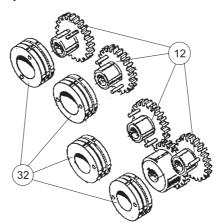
/7b Ersatzrollen Aluminium / spare part rolls aluminium
